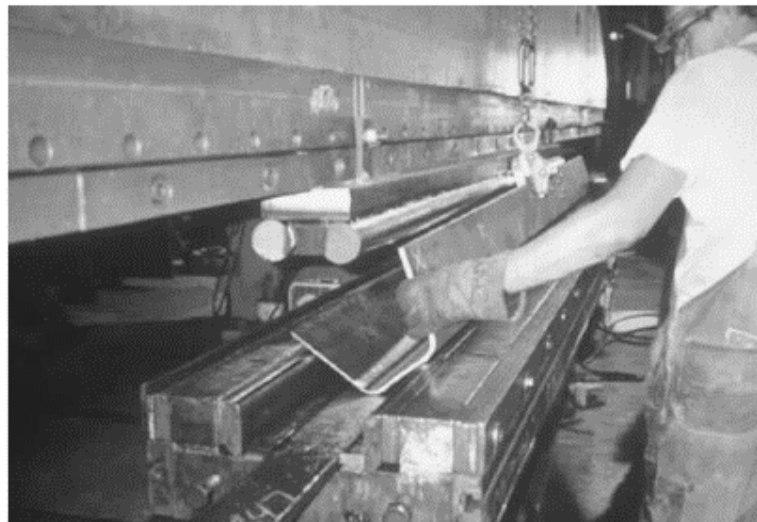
Fabricación Viga U simple, figura 14.2 Bridge Engineering Handbook, Wai-Fah Chen Lian Duan
